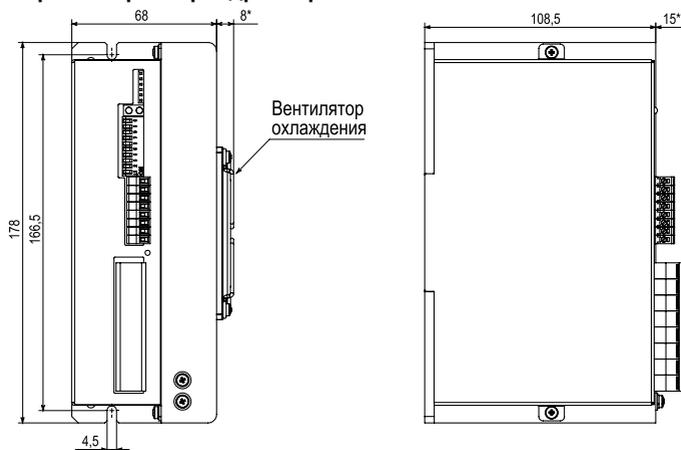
габаритные размеры драйверов SMD-20.42.60.TT
